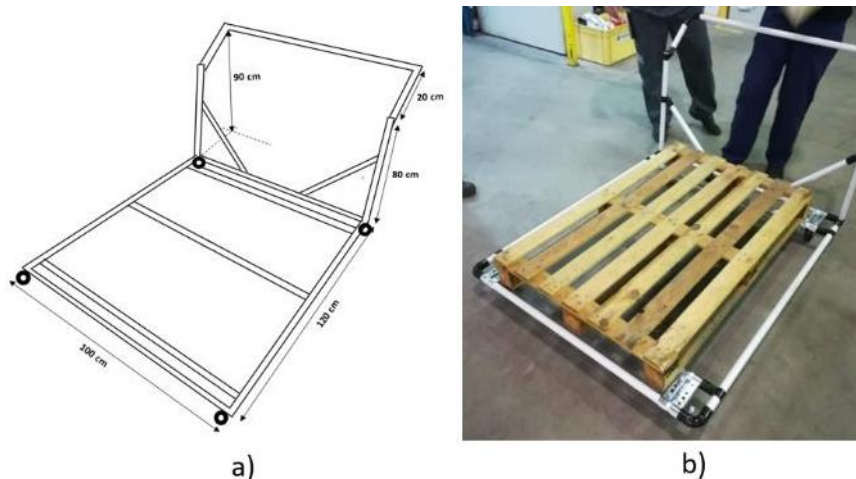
a) Esboço do carrinho de MP b) Carrinho de MP
